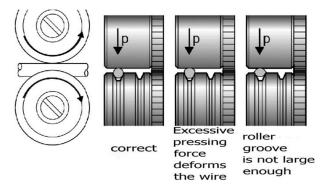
Impacto del rodillo en el alambre de soldadura
